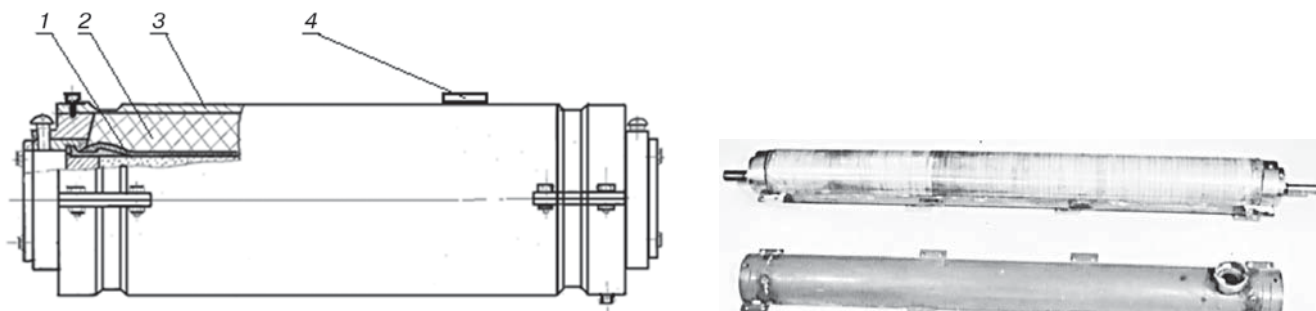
Пресс-форма для заливки ТИП на прямолинейный трубопровод:
